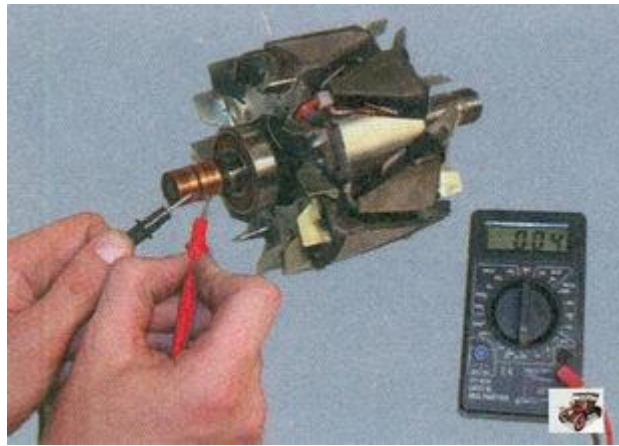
Проверка обмоток ротора на обрыв
